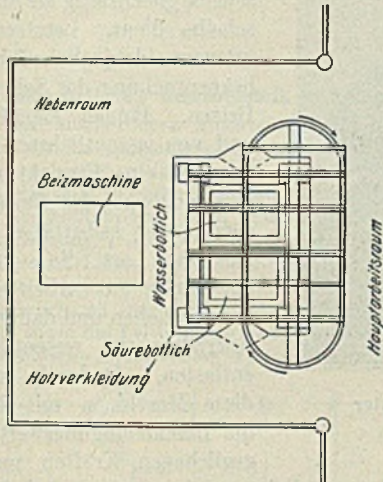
Grundriß einer elektrisch angetriebenen Blechbeizvorrichtung mit Rundbahn.
